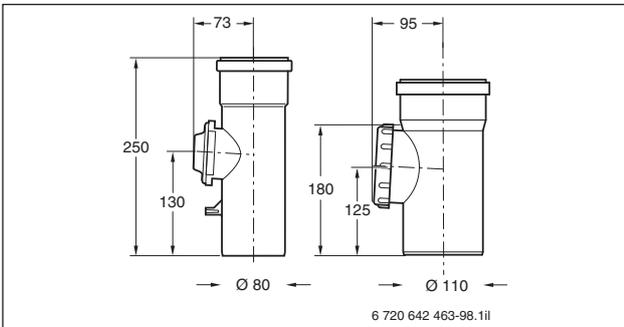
Rohr mit Prüföffnung (Maße in mm)
